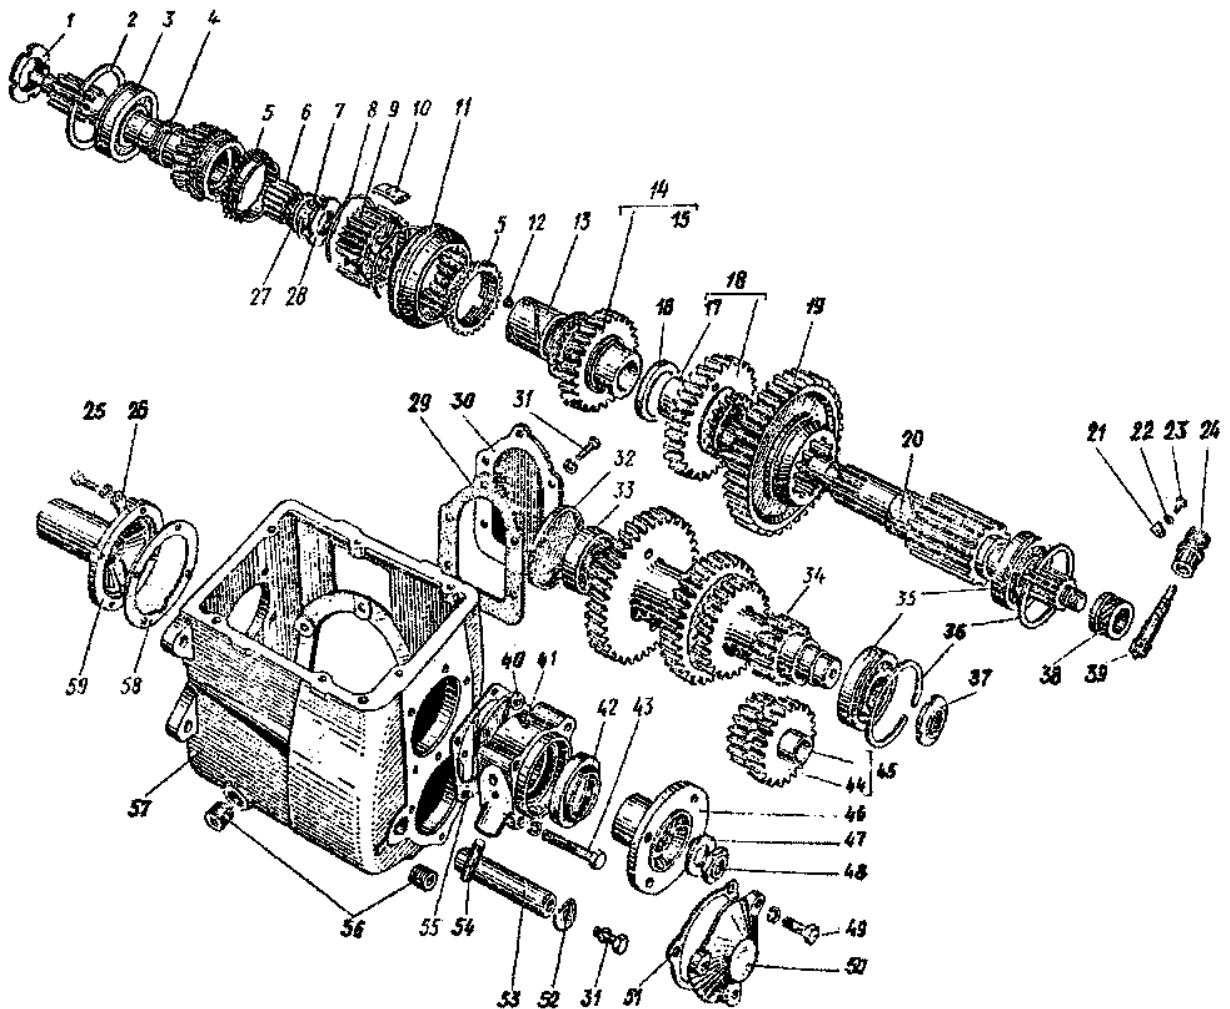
Загальний вигляд і взаємне розташування деталей коробки переміни передач автомобіля ГАЗ-53
